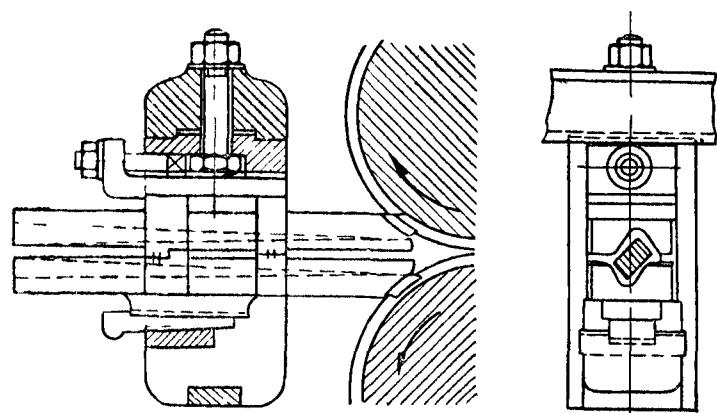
Схема кантующей проводки непрерывного заготовочного стана
